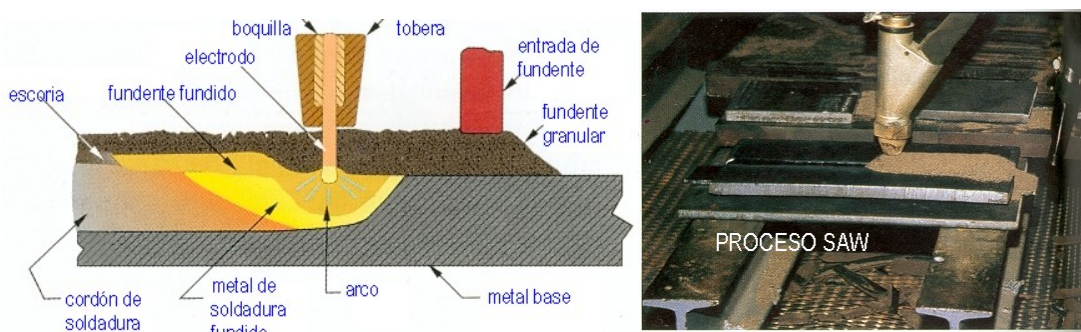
Proceso de soldadura por arco sumergido.
